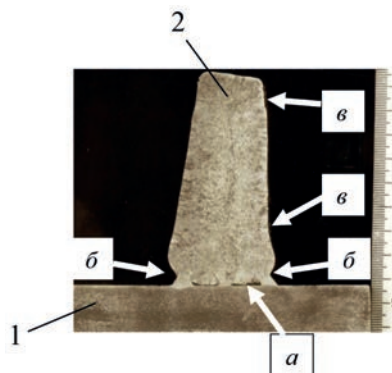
Поперечный макрошлиф опытного образца с дефектами: 1 – основной металл, 2 – наплавленный металл; стрелками показаны места несплошностей: некачественного формирования галтелей (б) и рабочей поверхности наплавленного металла (в)
